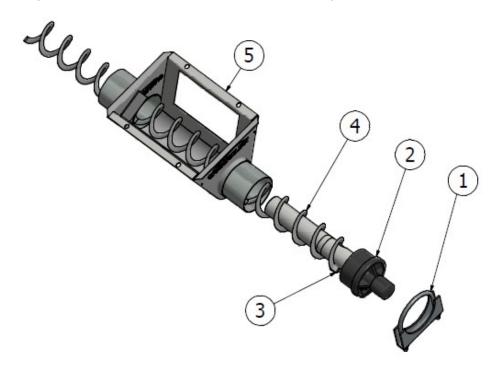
Модель 75, 90 и HR анкерный болт и подшипник
